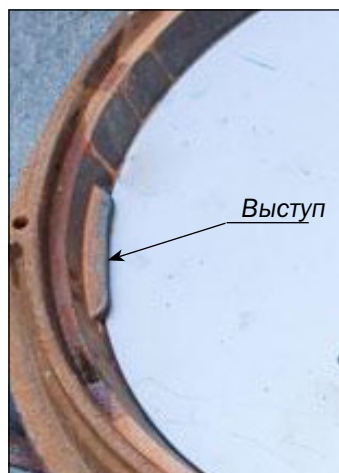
УЗНК, установленное в корпус люка под его выступ
